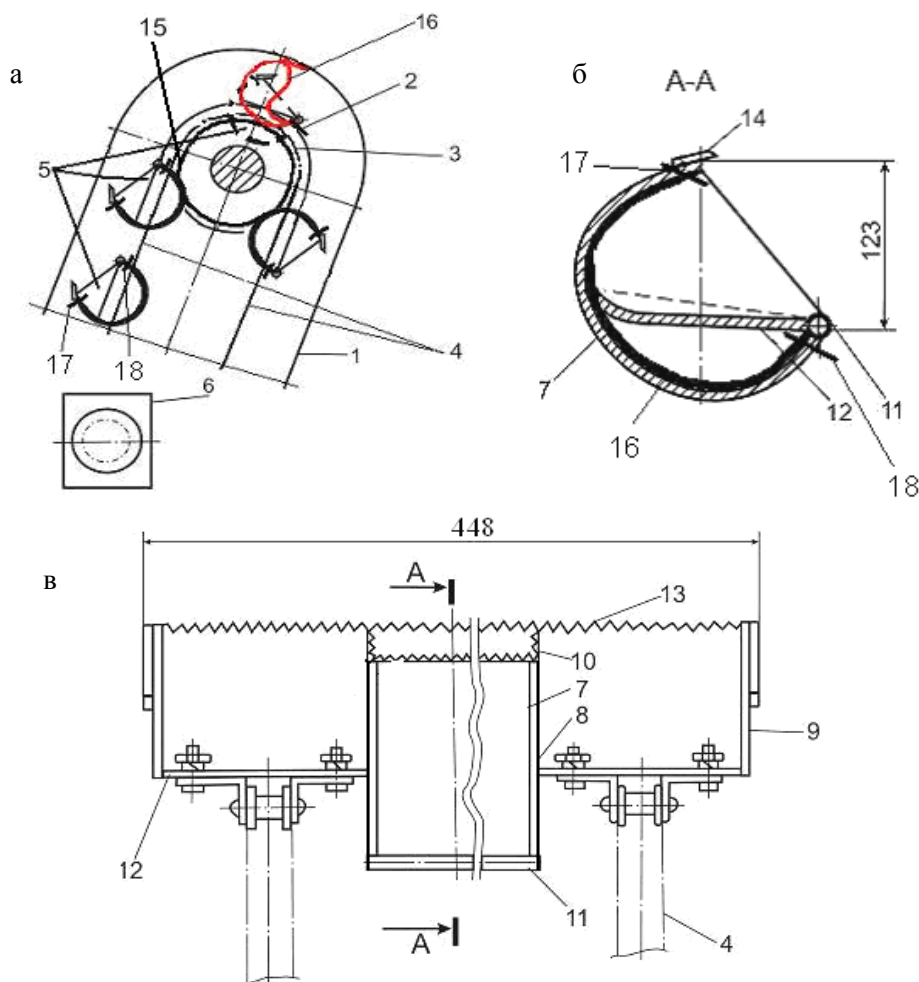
Ківшовий похилий дволанцюговий елеватор зі встановленими на ньому ковшами з рухомими днищами півкруглої форми з гнучкою стрічкою:
